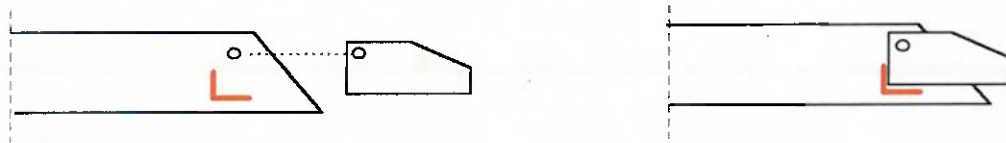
Esquema do projeto de encaixe da viga de engate
